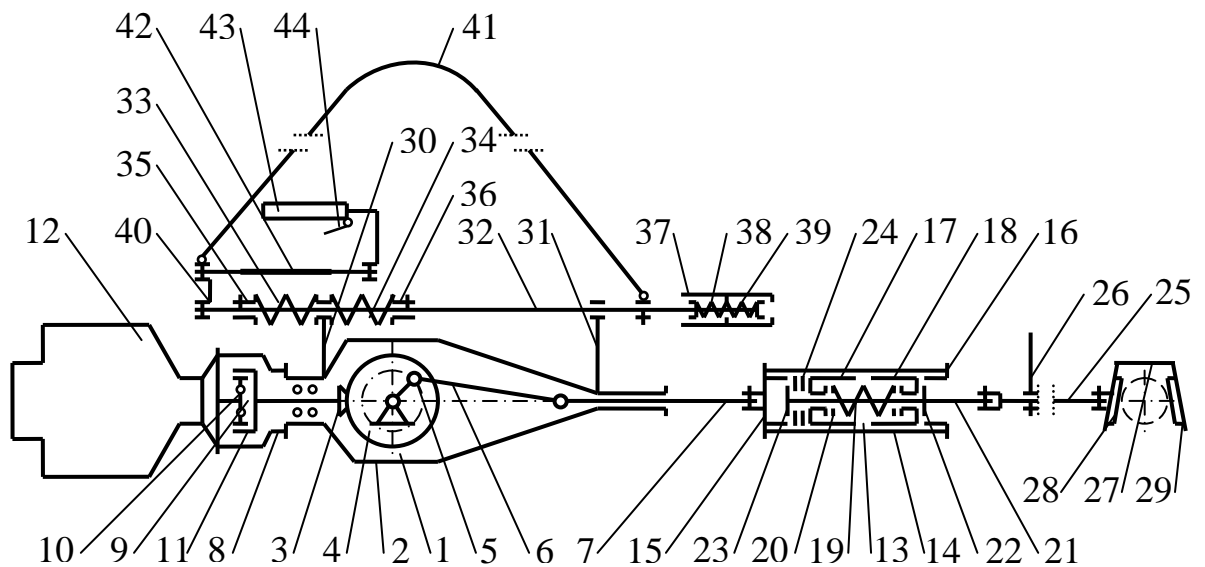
Принципова схема ручного віброударного струшувача плодів: 1 – збурювач коливань; 2 – корпус збурювача; 3, 4 – ведуча і ведена конічні шестерні; 5 – кривошип; 6 – шатун; 7 – повзун; 8 – корпус муфти; 9 – відцентрова муфта; 10, 11 – ведуча та ведена частини муфти; 12 – двигун внутрішнього згоряння; 13 – ударний механізм; 14 – циліндр; 15, 16 – кришки-упори; 17, 18 – ковзні чашки; 19 – пружина; 20, 24 – регулювальні шайби; 21 – ковзний шток; 22, 23 – упори; 25 – штанга; 26 – важіль повертання штанги; 27 – вилчастий захват; 28, 29 – еластичні подушки; 30, 31 – кронштейни; 32 – напрямна штанга; 33, 34, 38, 39 – демпферні пружини; 35, 36 – упори; 37, 43 – рукоятки; 40 – поперечний важіль; 41 – утримувальна лямка; 42 – еластична вставка; 44 – важілець управління системою подачі палива двигуна внутрішнього згоряння
